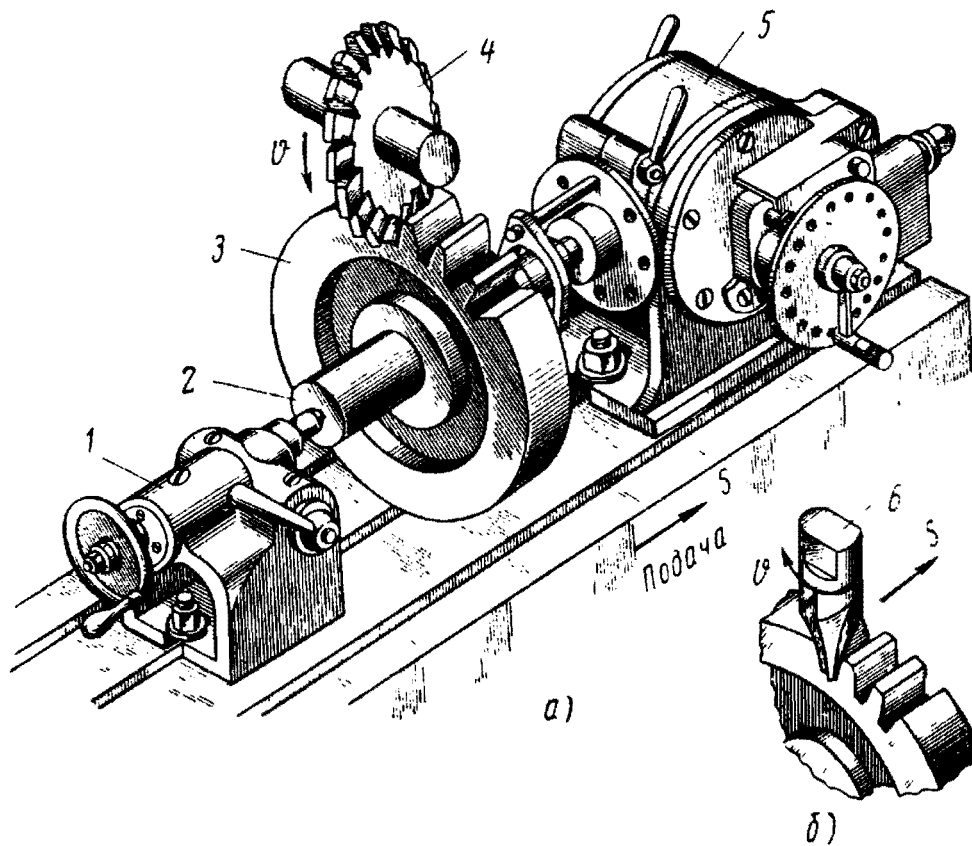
Схема нарезания зубчатого колеса на горизонтально-фрезерном станке:
